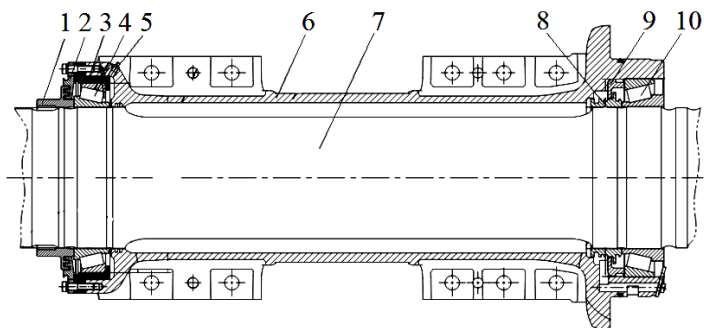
Устройство моторно-осевого подшипника электровоза БКГ-1
